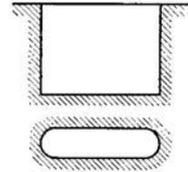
Langloch, hergestellt auf Langlochbohrmaschine.
